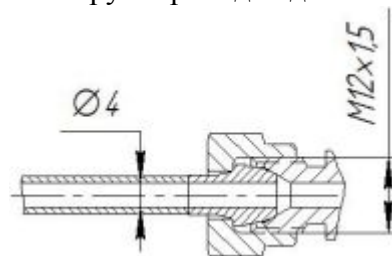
Стык трубопровода 4-НК7-96, 4-НК7-104 с ответным штуцером
